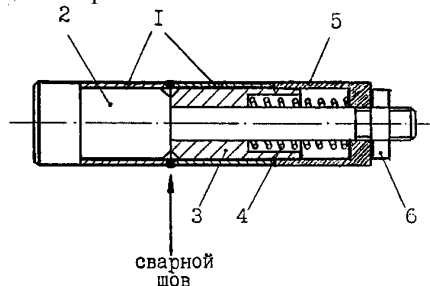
Схема приспособления для изготовления образцов сварных соединений трубок из КТЦ-110: 1 - свариваемые патрубки; 2 - концевая оправка; 3 - тулочная оправка; 4 - поджимная пружина; 5 - поджимной колпачок; 6 - гайка
